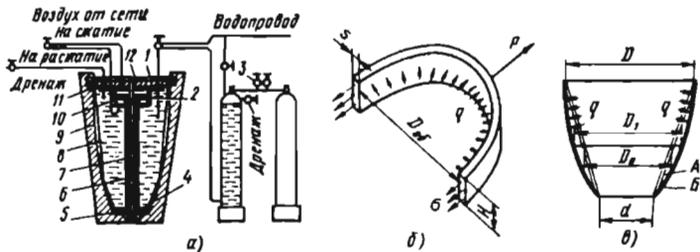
Схема формовки обечаек жидкостью: а — схема установки; б — схема действия сил; в — схема процесса формообразования; А — заготовка; Б — готовая обечайка
